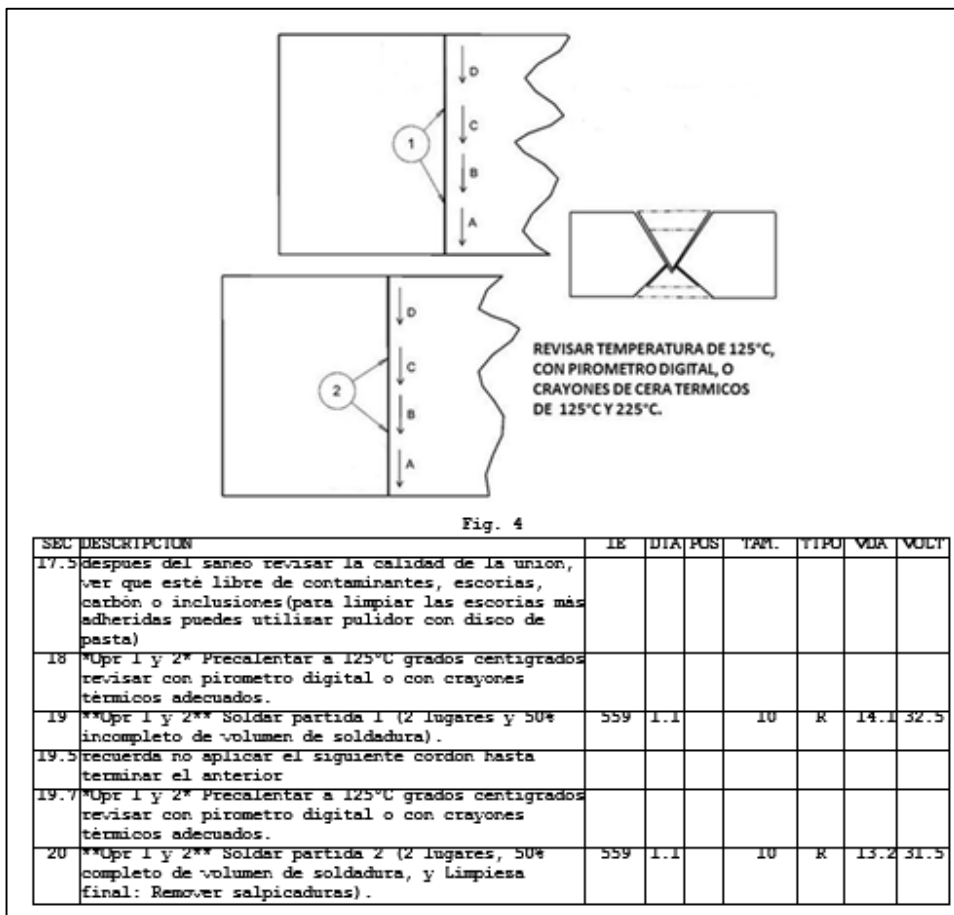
11 Últimos pasos de la operación de soldadura final de los pisos (cortesía de la compañía fabricante de cajas para camión).
